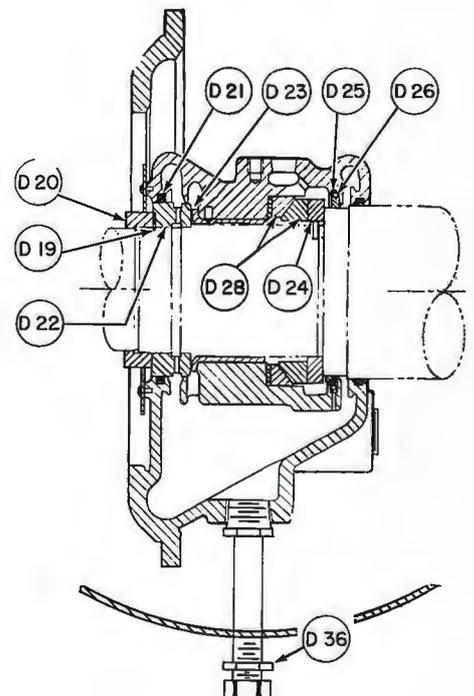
Hauptlager (Maschine-Typen 6, 7, 8)
